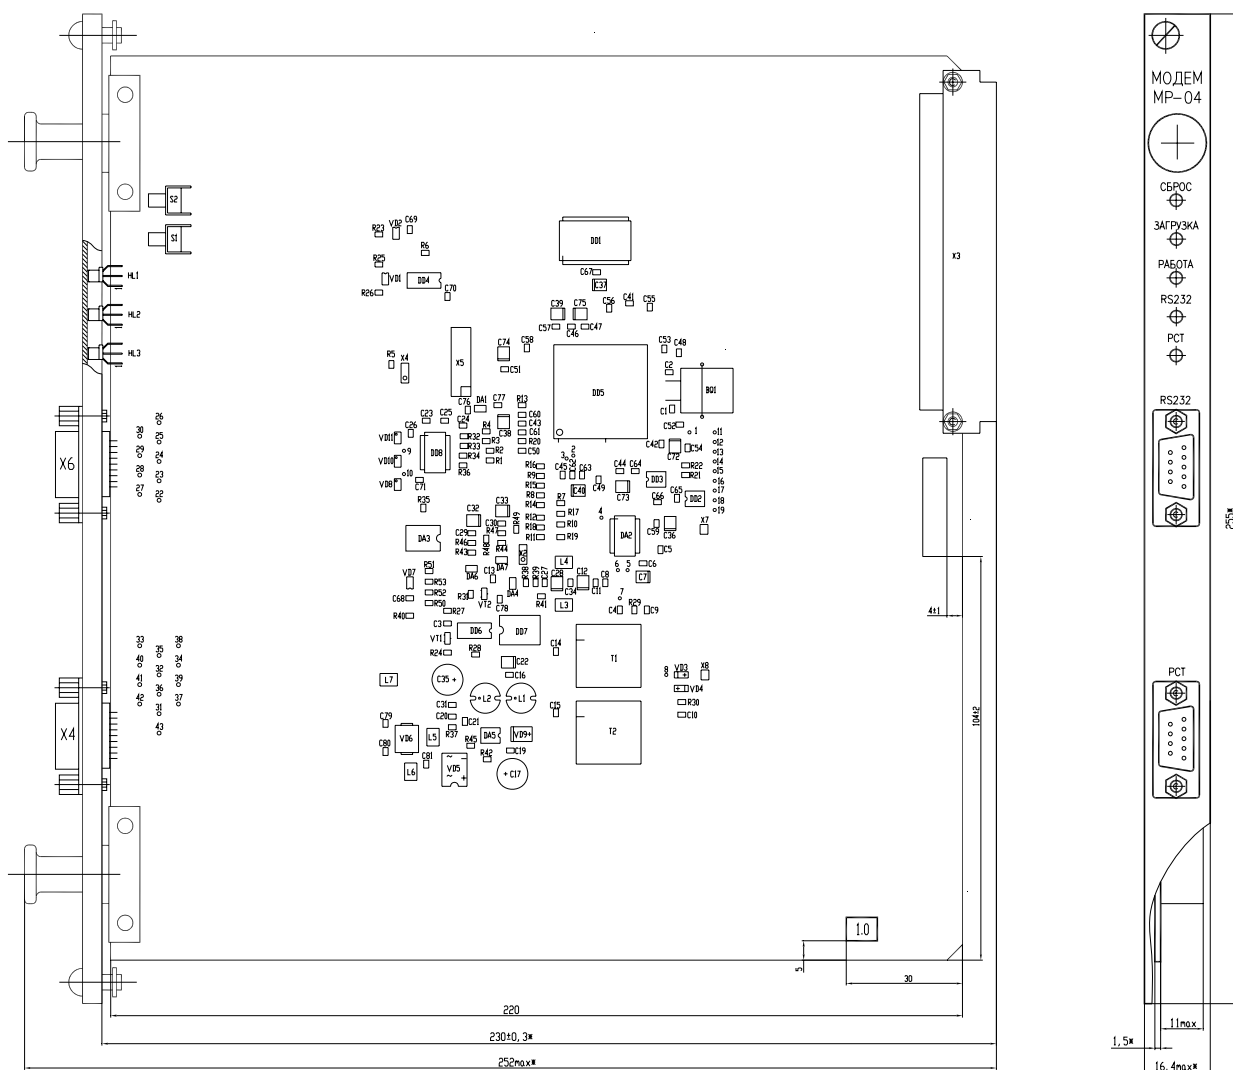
Внешний вид и габаритные размеры модема МР-04.02
